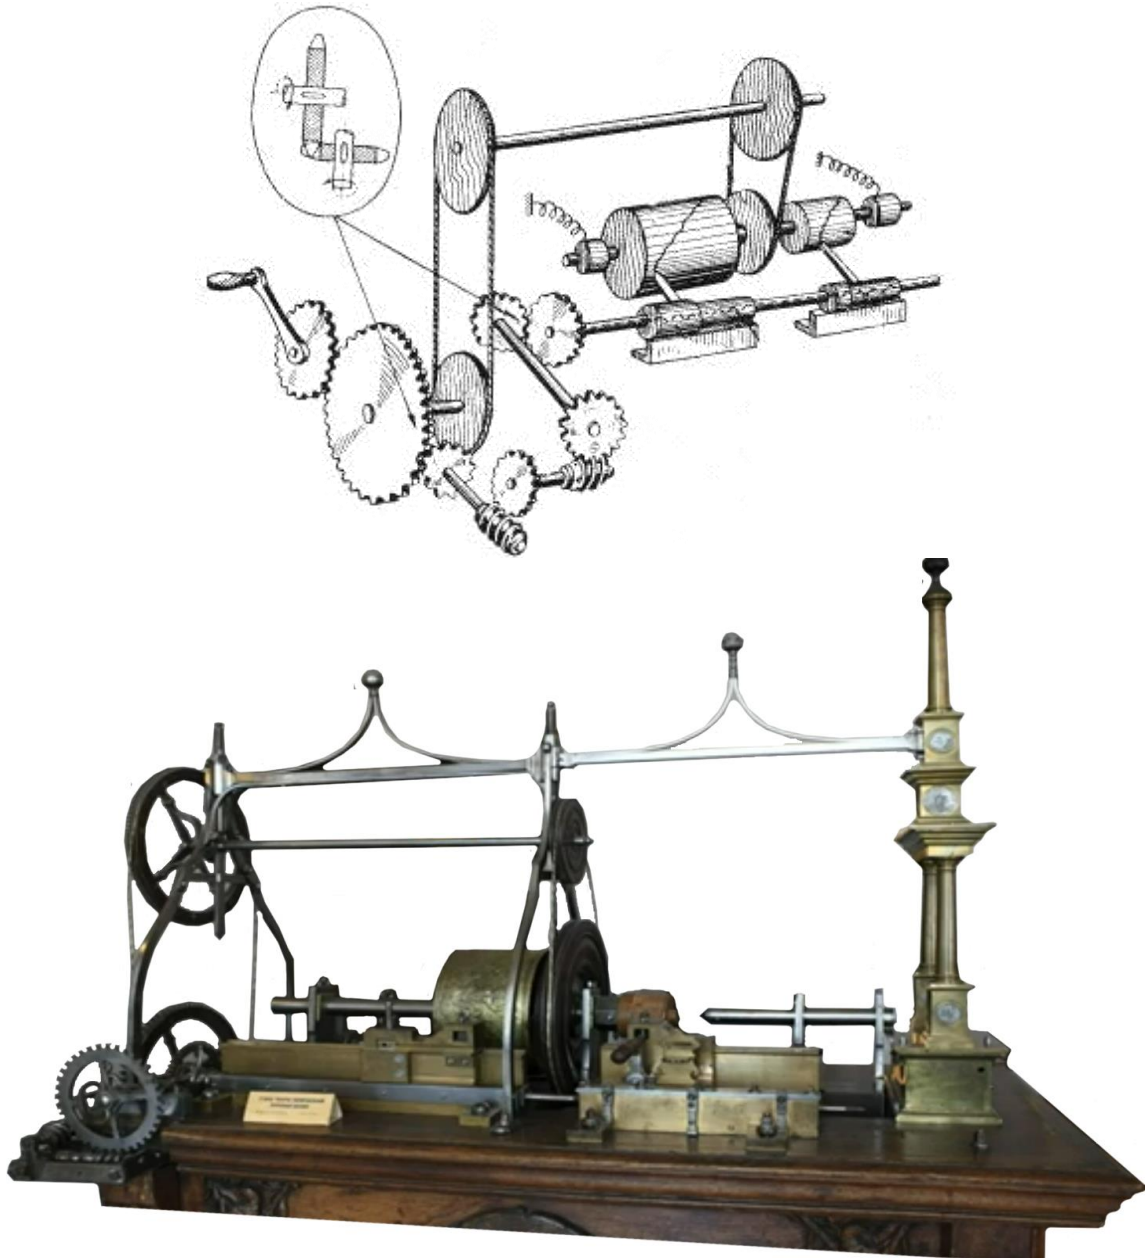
Схема та зовнішній вигляд токарного станка Нартова А.К.
